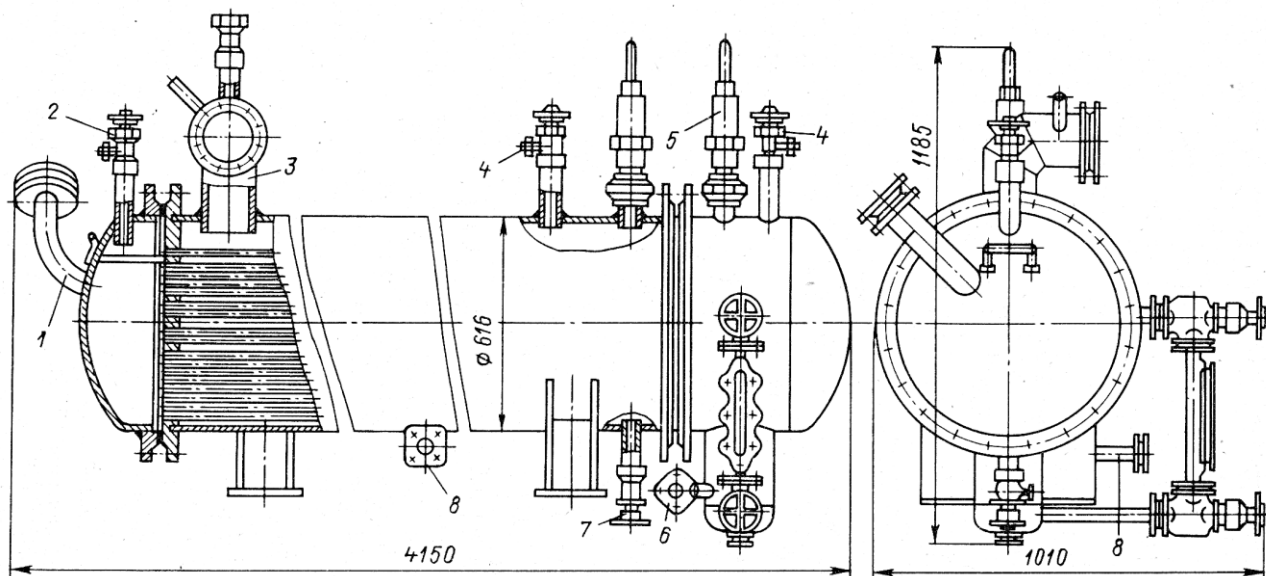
Горизонтальний кожухотрубний конденсатор-випарник
